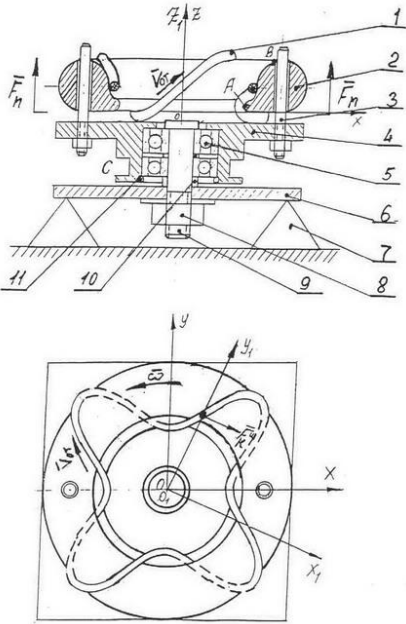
Тороидальный летательный аппарат-инерциод конструкции В.И. Докучаева (1996г). Сборочный чертёж.
